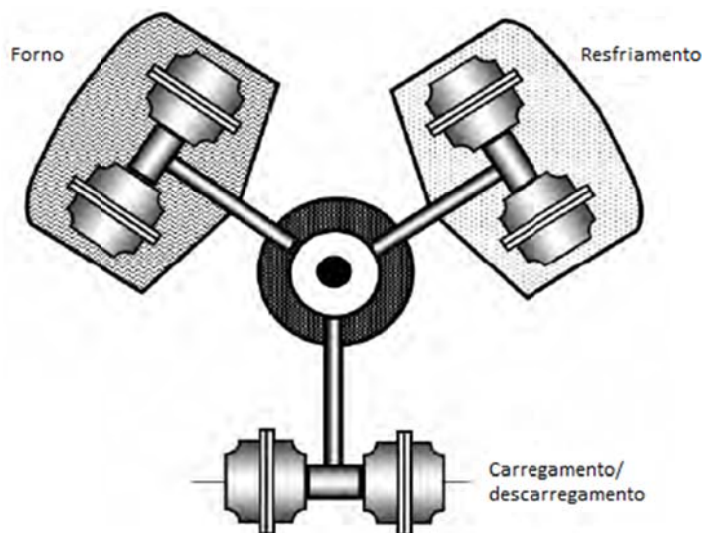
Máquina de rotomoldagem do tipo carrossel.
